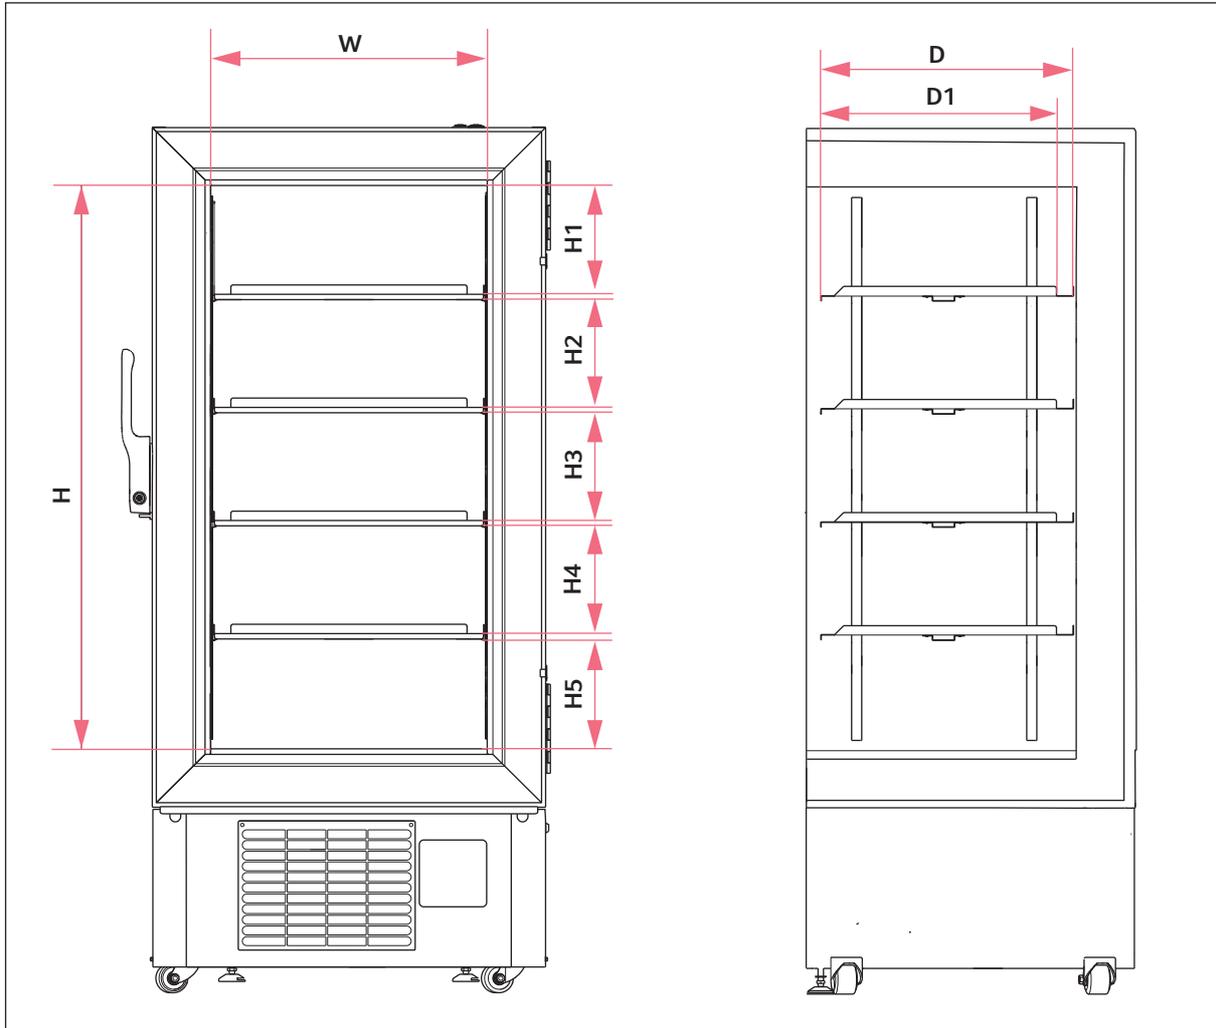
Innenmaße CryoCube F440n und CryoCube F440h
